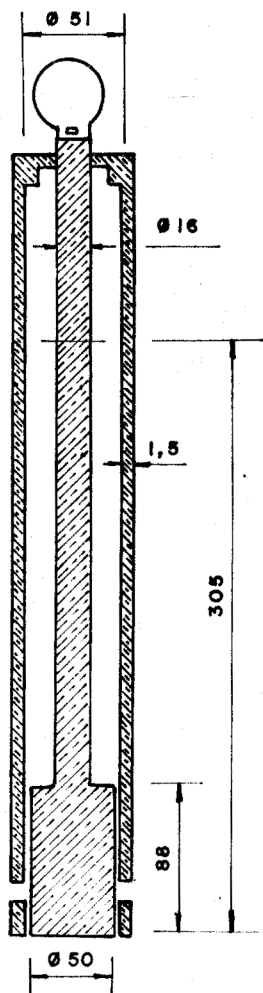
DIMENSÕES DO SOQUETE METÁLICO
